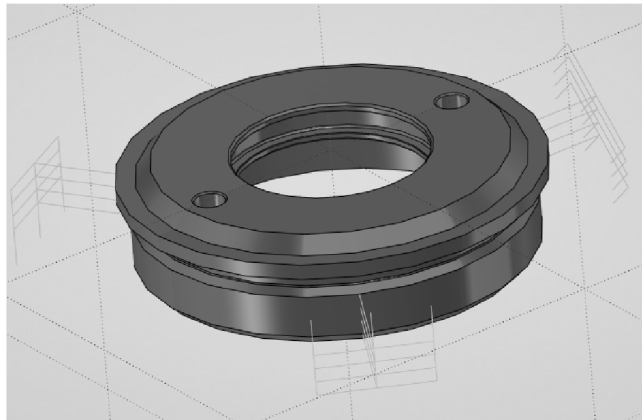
Вибір поверхонь моделі деталі для закріплення
